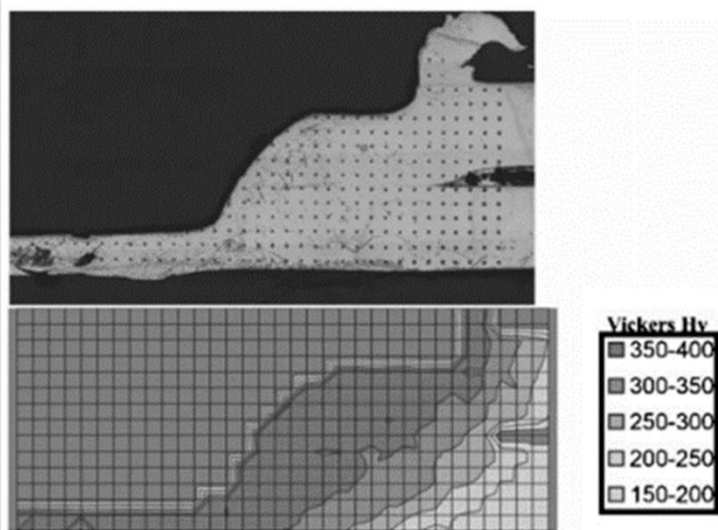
Perfil de dureza no ponto de solda de alumínio 6061-T6 em processo de FSSW
